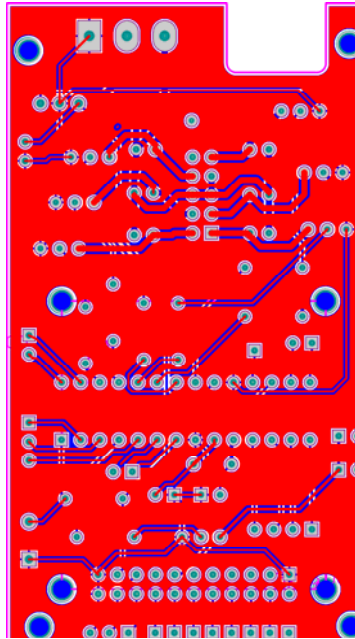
Diseño electrónico de la PCB del dispositivo de la alternativa 2.
